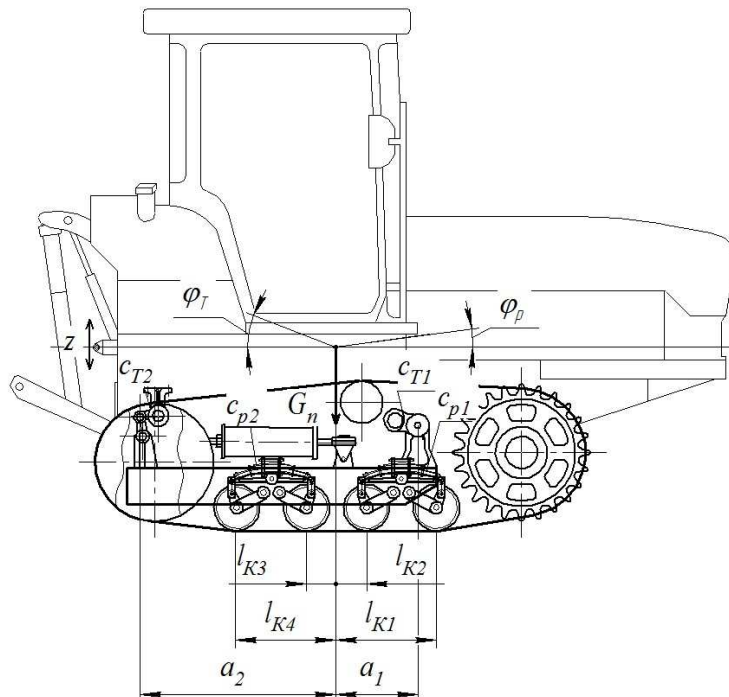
Схема к определению частот колебаний подрессоренной части корпуса трактора
